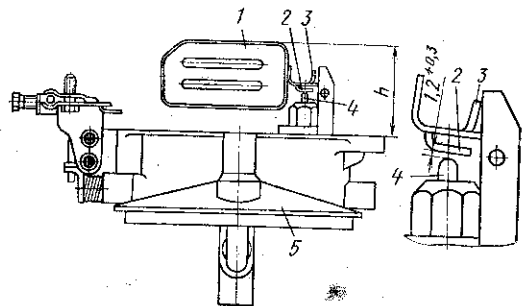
Проверка установки поплавка на крышке поплавковой камеры карбюратора К-126Н:
